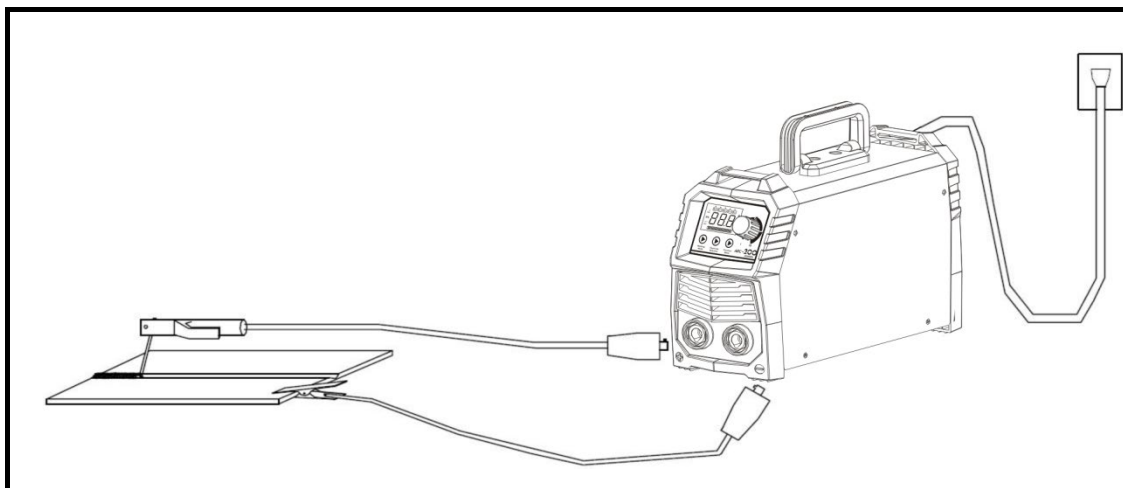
Diagrama esquemático da soldadura de MMA
